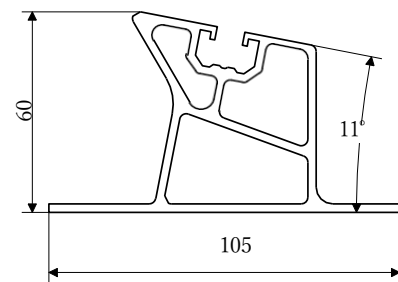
Suport de montare din aluminiu K-45-8, joasă
